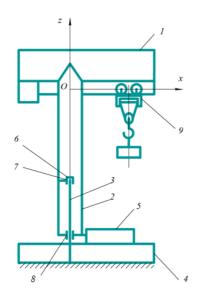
Кинематическая схема консольного крана на колонне: 1 – стрела; 2 - гильза; 3 - колонна; 4 - опорная рама; 5 - механизм поворота; 6, 7, 8 - подшипники; 9 - тележка
